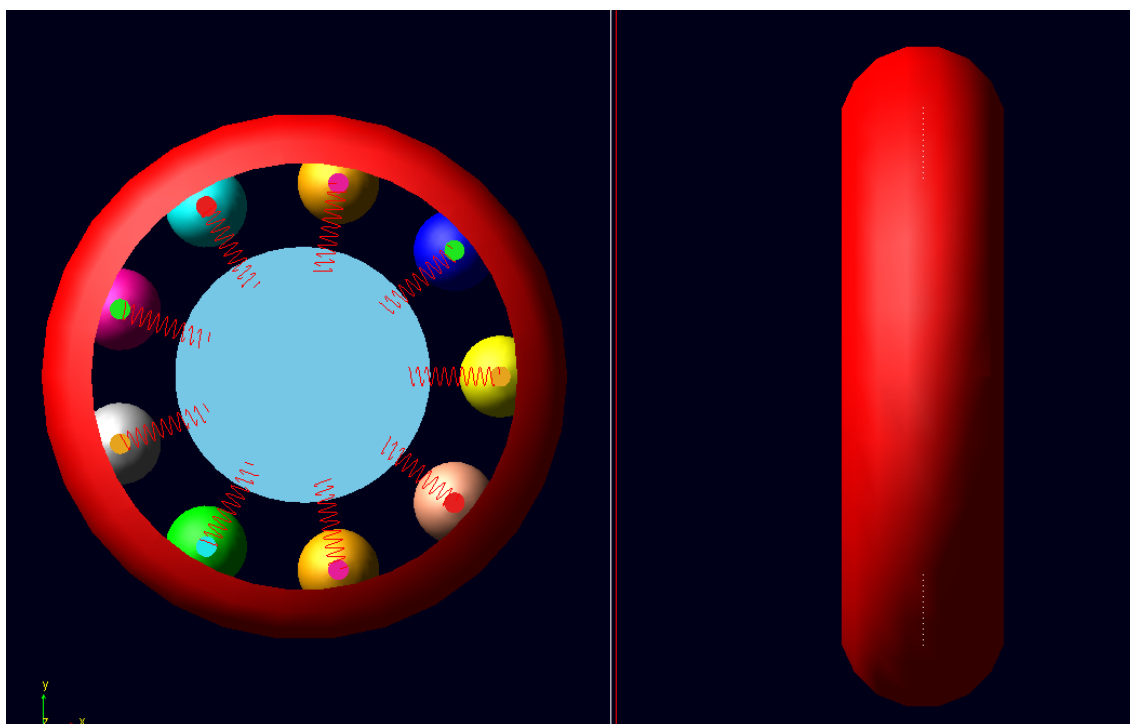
Alzado y perfil del rodamiento de 9 bolas
